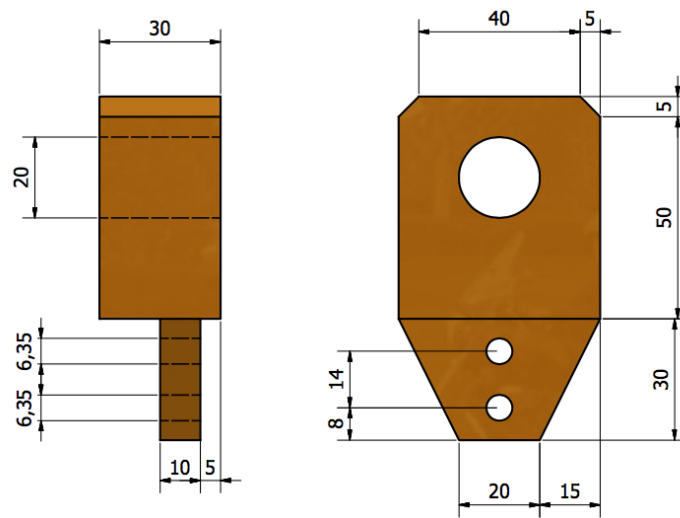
DIMENSIONES UNIÓN MANIVELA Y EJE CONECTOR
